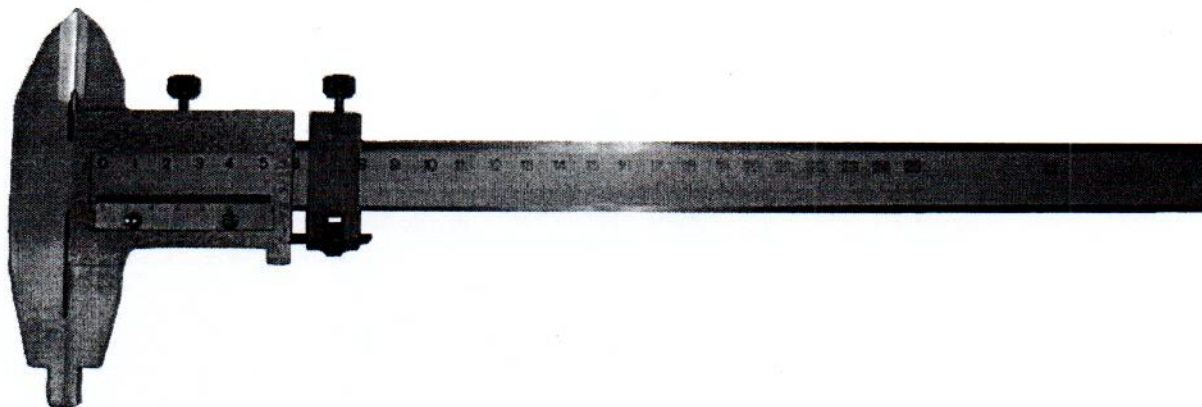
Внешний вид штангенциркуля типа ШЦ-II
